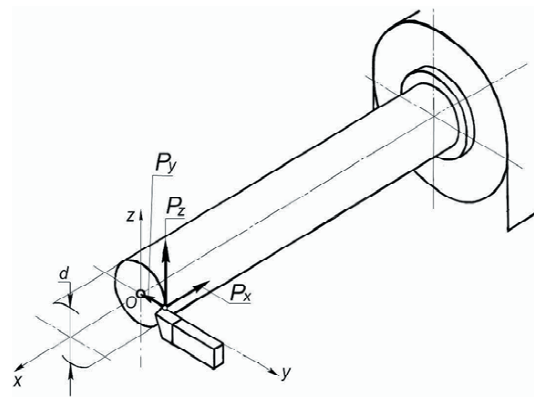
Класична обробка заготовки одним різцем на токарному верстаті
